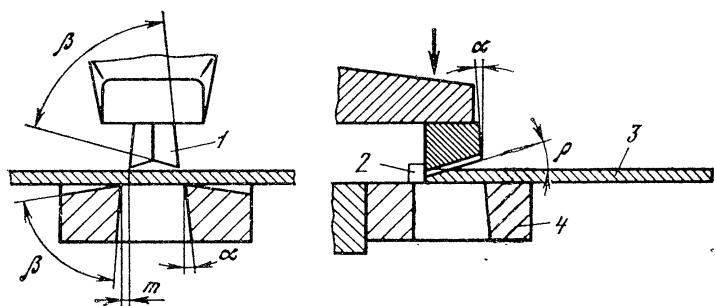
Схема приспособления для нарезания зубьев ручных пил:
